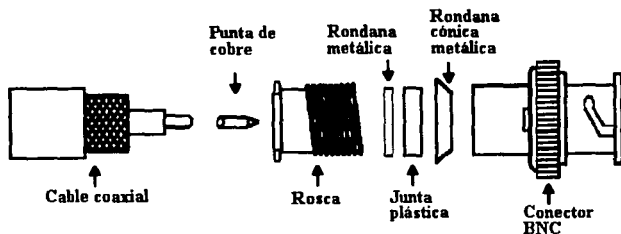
Instalación de un cable coaxial al conector BNC
